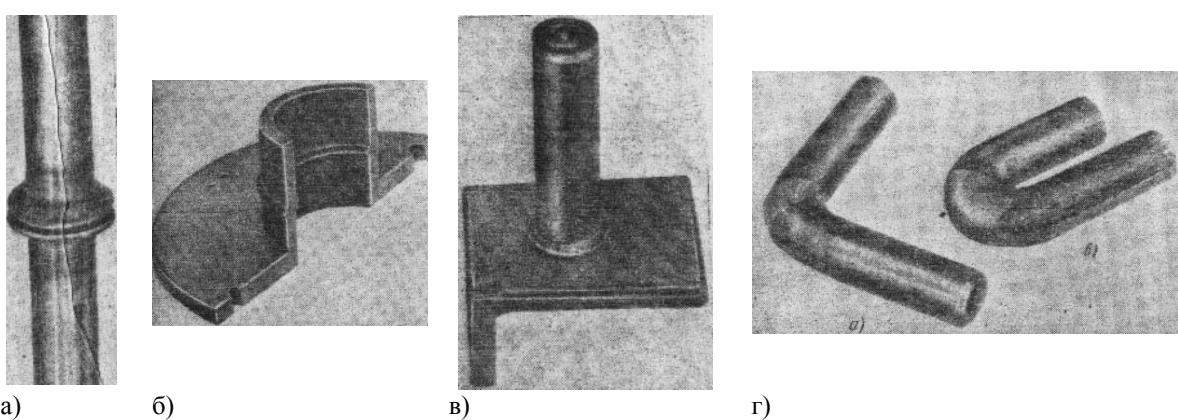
Зварка тертям: а) стержнів; б) фланця;
